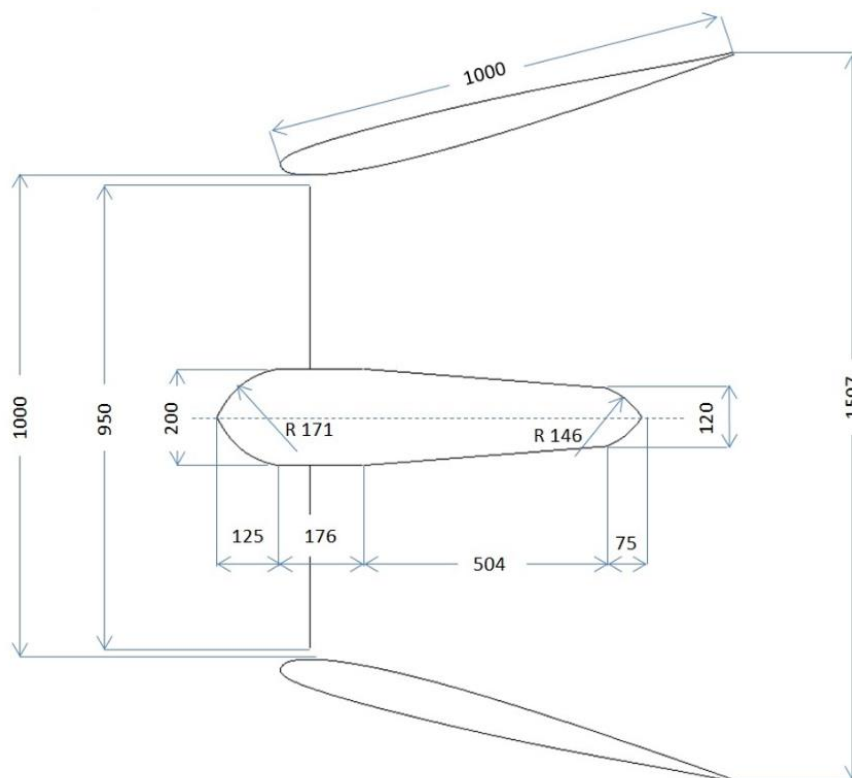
Dimensões Básicas da Turbina (em milímetros)
